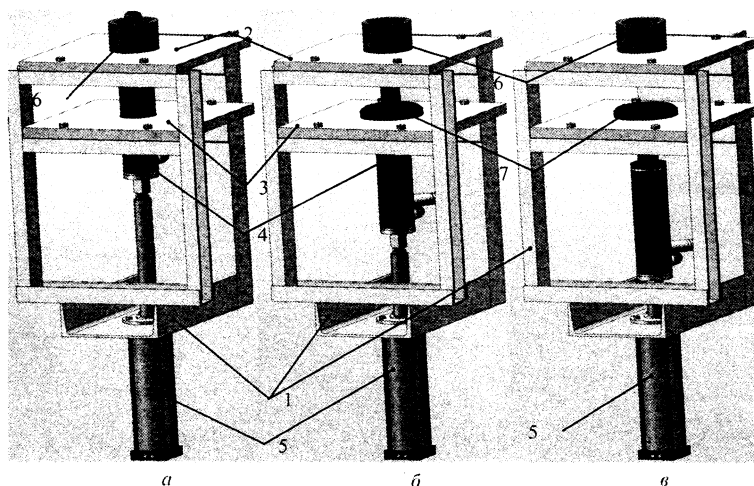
Твердотельная электронная модель тянущего устройства: а – первая стадия цикла работы установки; б – вторая стадия; в – третья стадия: 1 – сварная рама; 2 – верхняя плита; 3 – нижняя плита; 4 – внутренний кристаллизатор (дорн); 5 – гидроцилиндр; 6 – наружная втулка; 7 – опорное кольцо
